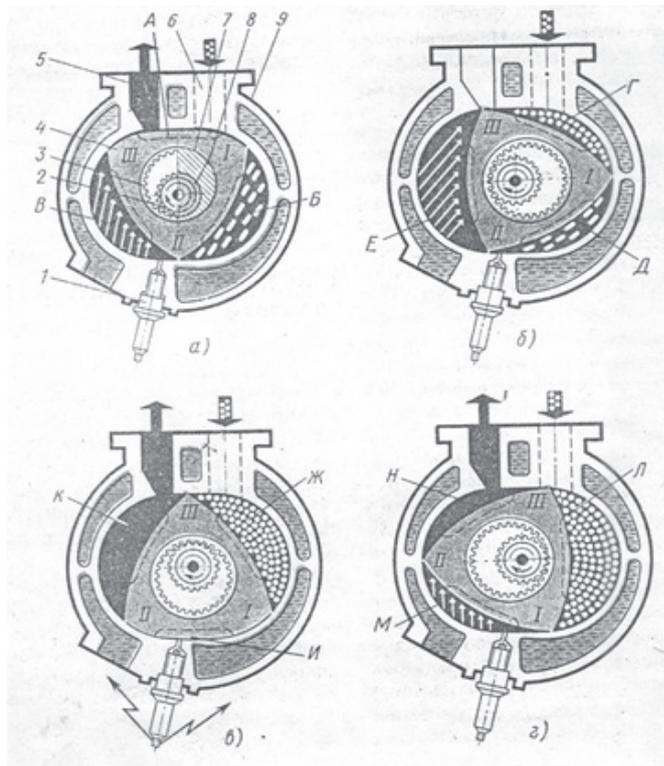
Схема и принцип работы роторно-поршневого двигателя:
